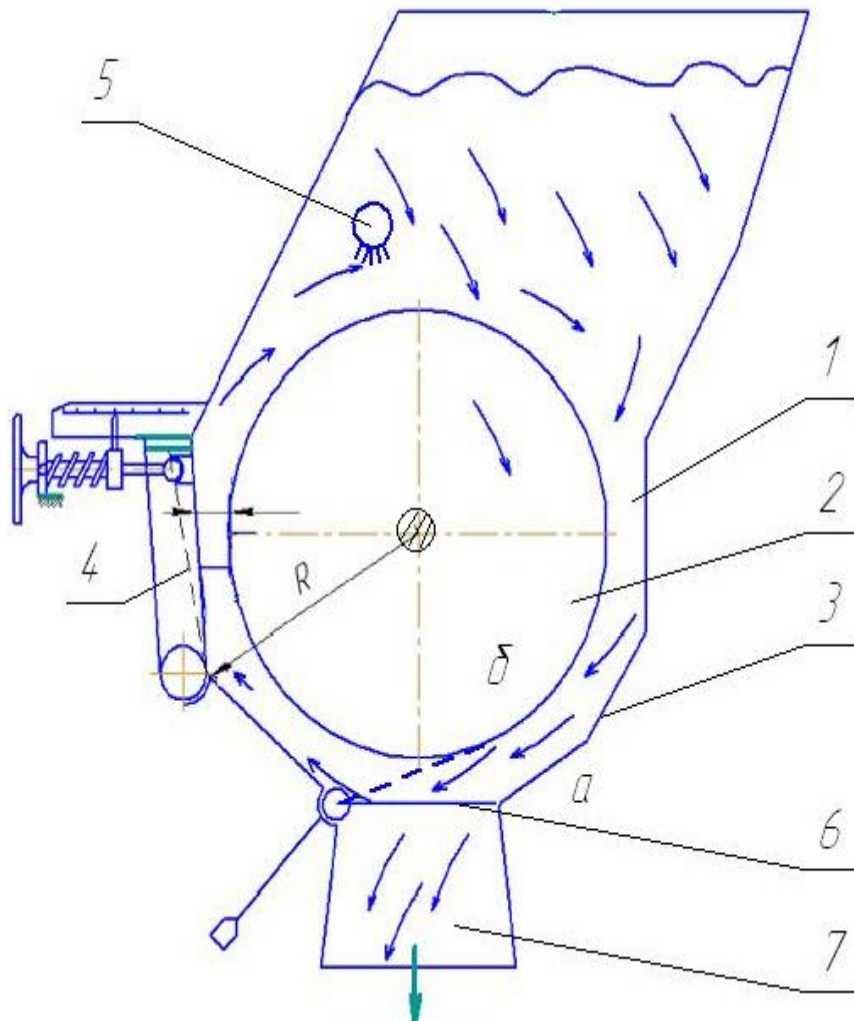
Схема поперечного перерізу машини: 1 – робоча камера; 2 – рифлений місильний барабан; 3 – боковини у вигляді багатогранника; 4 – регулятор з стабілізатором консистенції; 5 – подавач рідких компонентів; 6 – шибер для розвантаження; 7 – патрубок для розвантаження тіста
